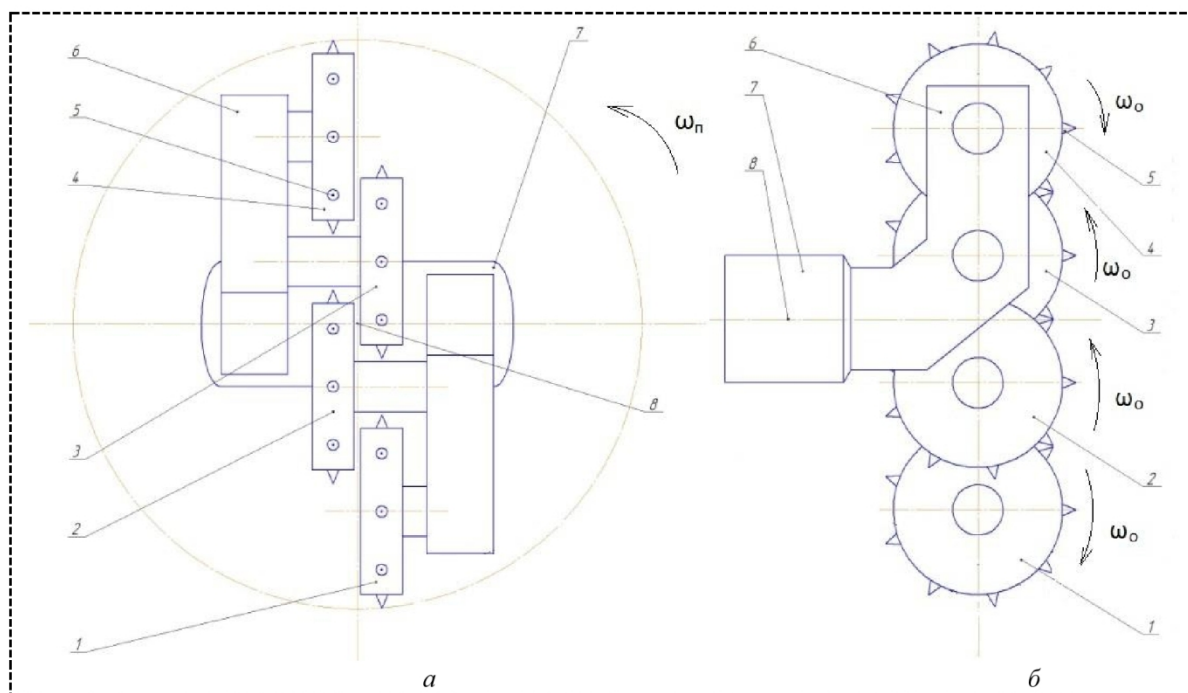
Схема исполнительного органа: а – вид спереди; б – вид сбоку
